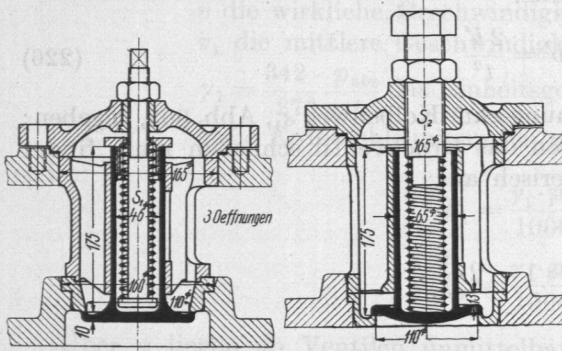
Saug- und Druckventil eines Kompressors (ältere Ausführung).
